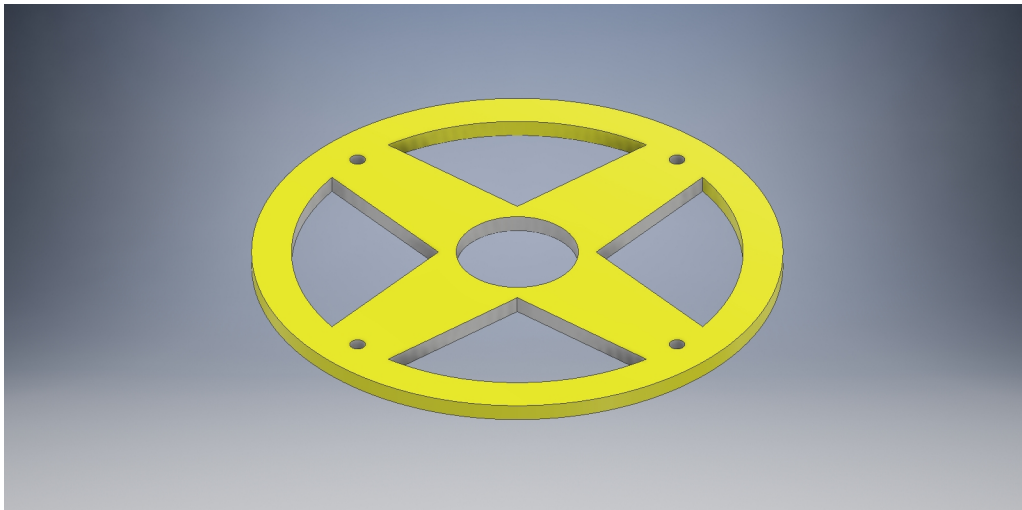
Soporte superior para la placa secundaria del diseño mecánico del dispositivo esclavo
